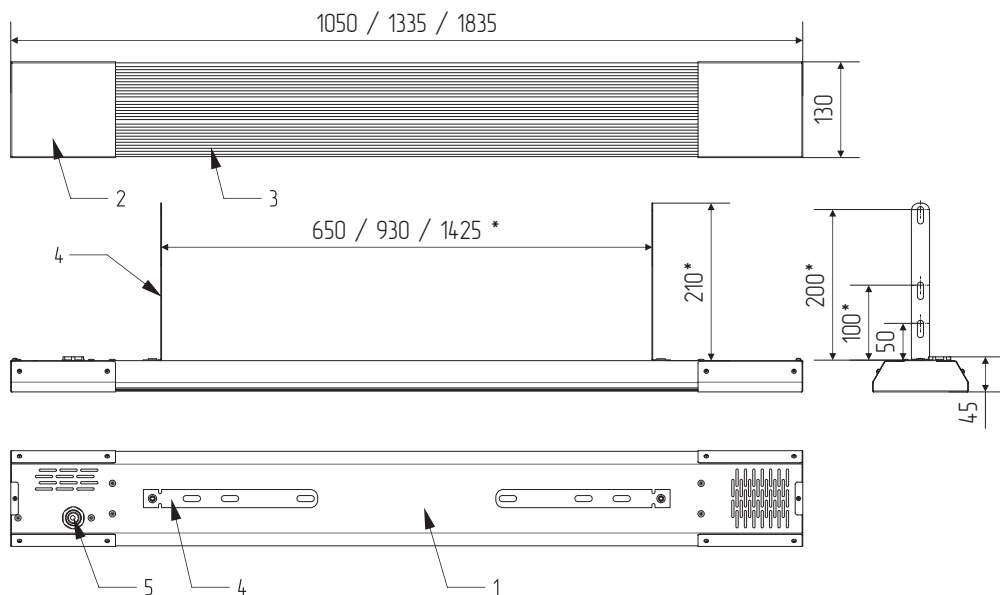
Габаритный чертёж и элементы конструкции инфракрасного обогревателя ТКИ-800 / ТКИ-1000 / ТКИ-1500.
